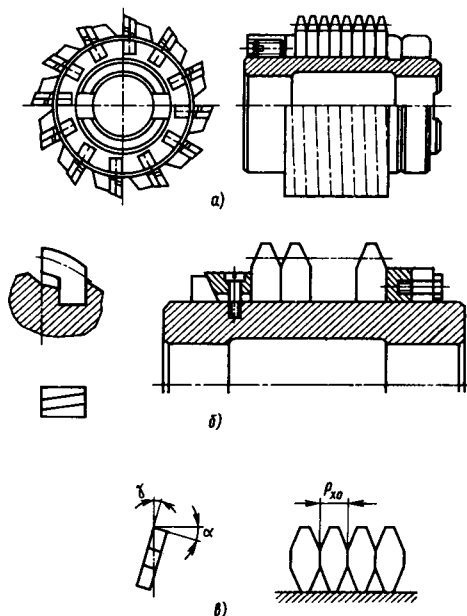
Червячные фрезы, оснащенные пластинами из твердого сплава
